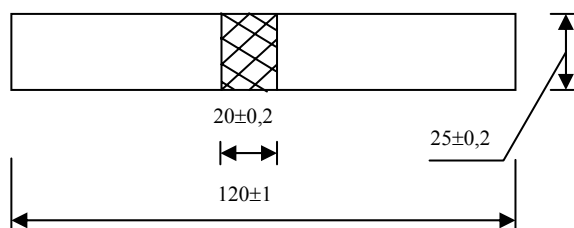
Образец для длительных испытаний на поперечный изгиб
